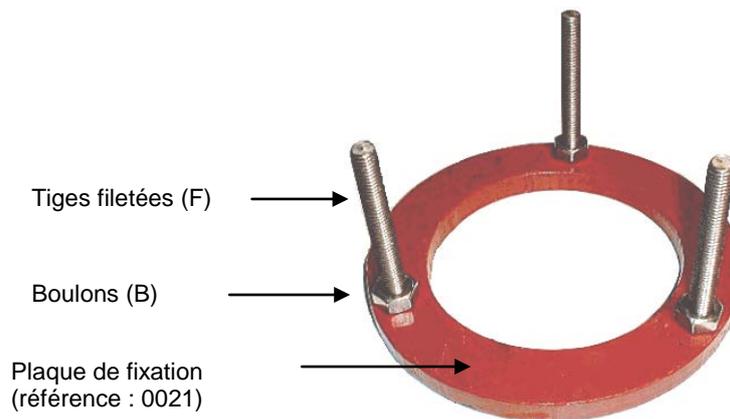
plaque de fixation prête à accueillir la bague de serrage
